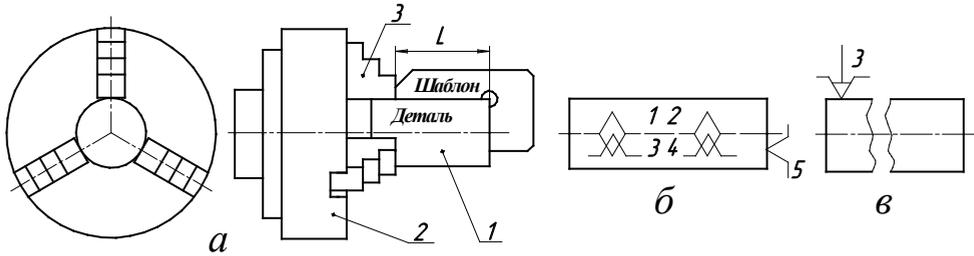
Установка заготовки в самоцентрирующем трехкулачковом патроне
